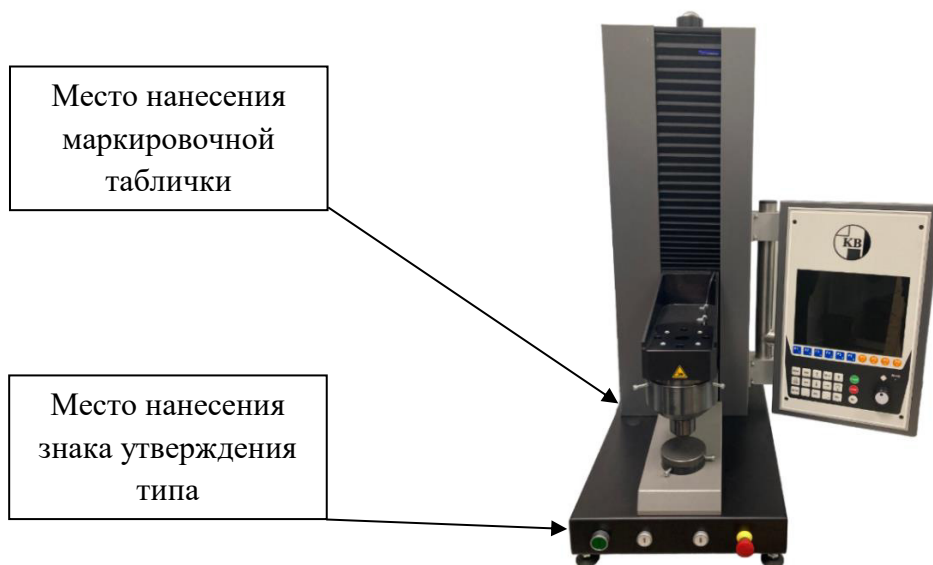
Общий вид твердомеров Роквелла КВЕ 150 R
